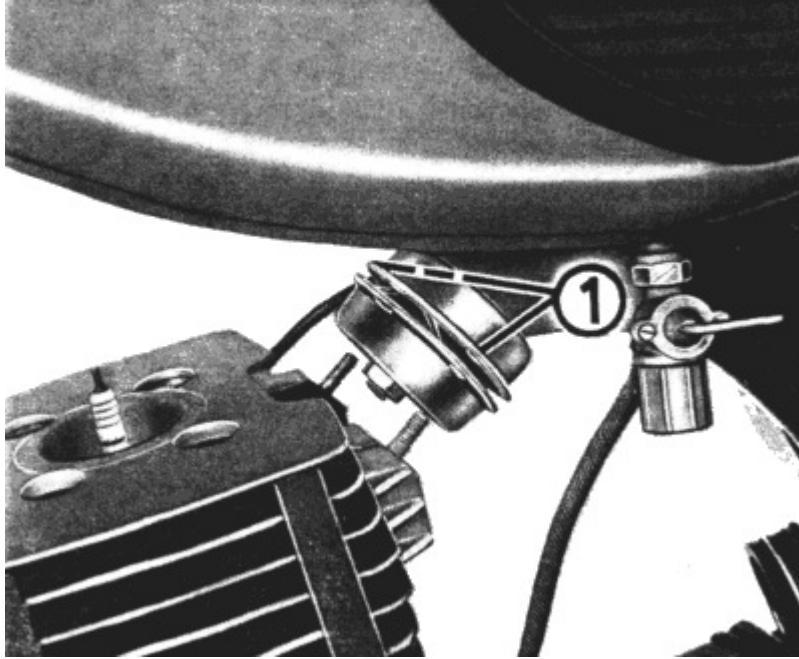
Auswechseln der elastischen Motoraufhängung am Zylinderdeckel
